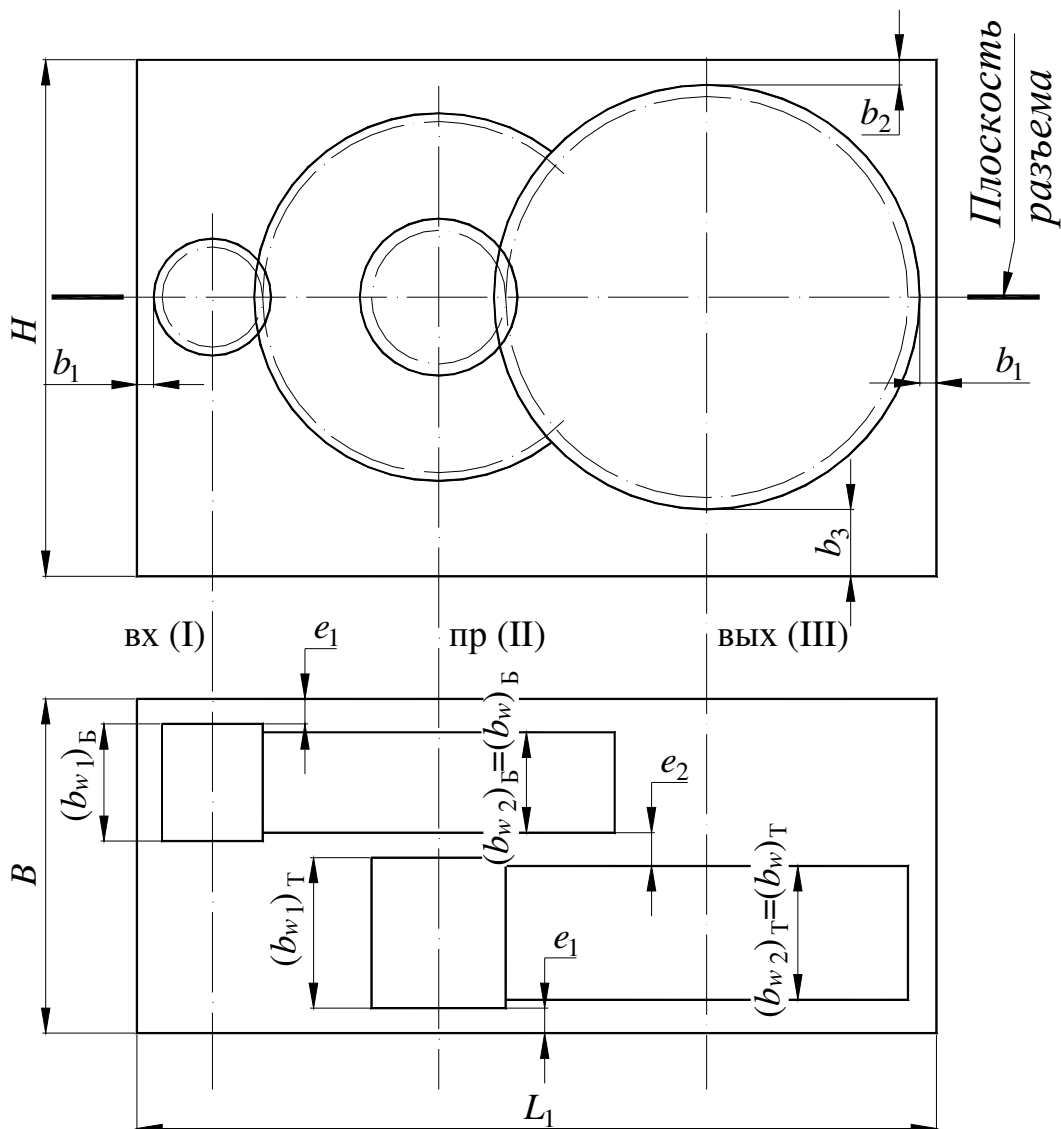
Первый этап эскизной компоновки двухступенчатого цилиндрического редуктора по развернутой схеме
